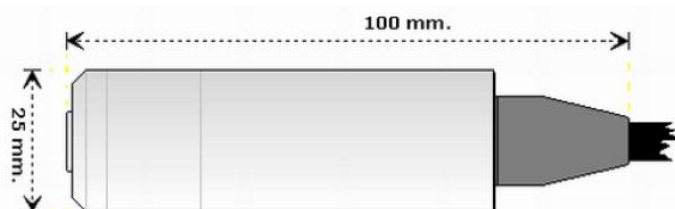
Schema di un sensore di pressione piezoelettrico.
